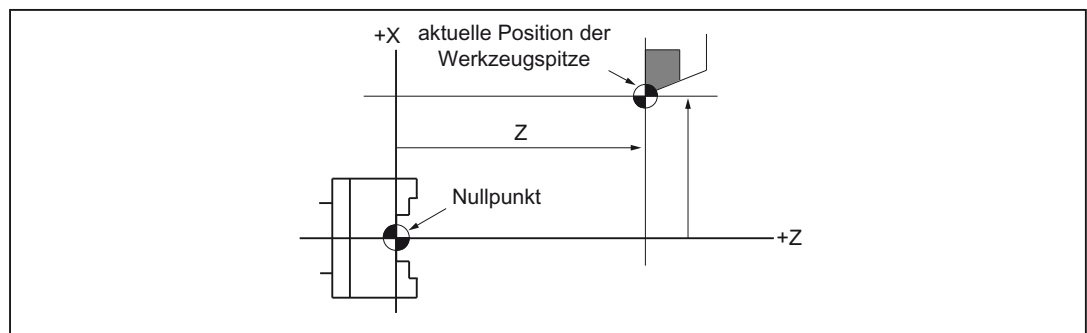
Mit X... Z.. angegebene Werkzeuglage
